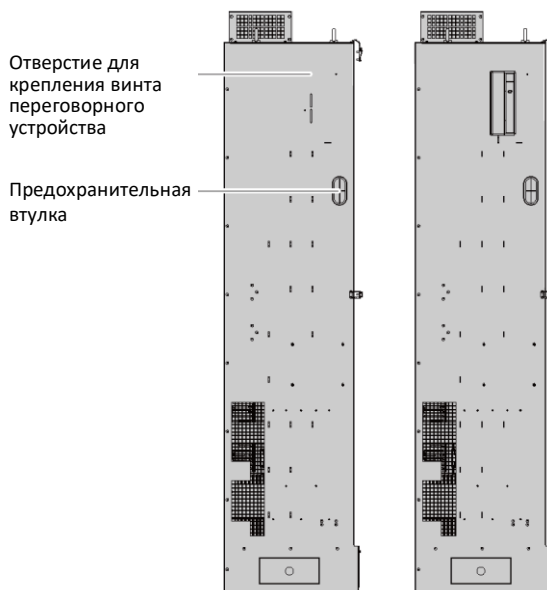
Установка переговорного устройства для шкафа управления MR (45 кВт - 110 кВт)
